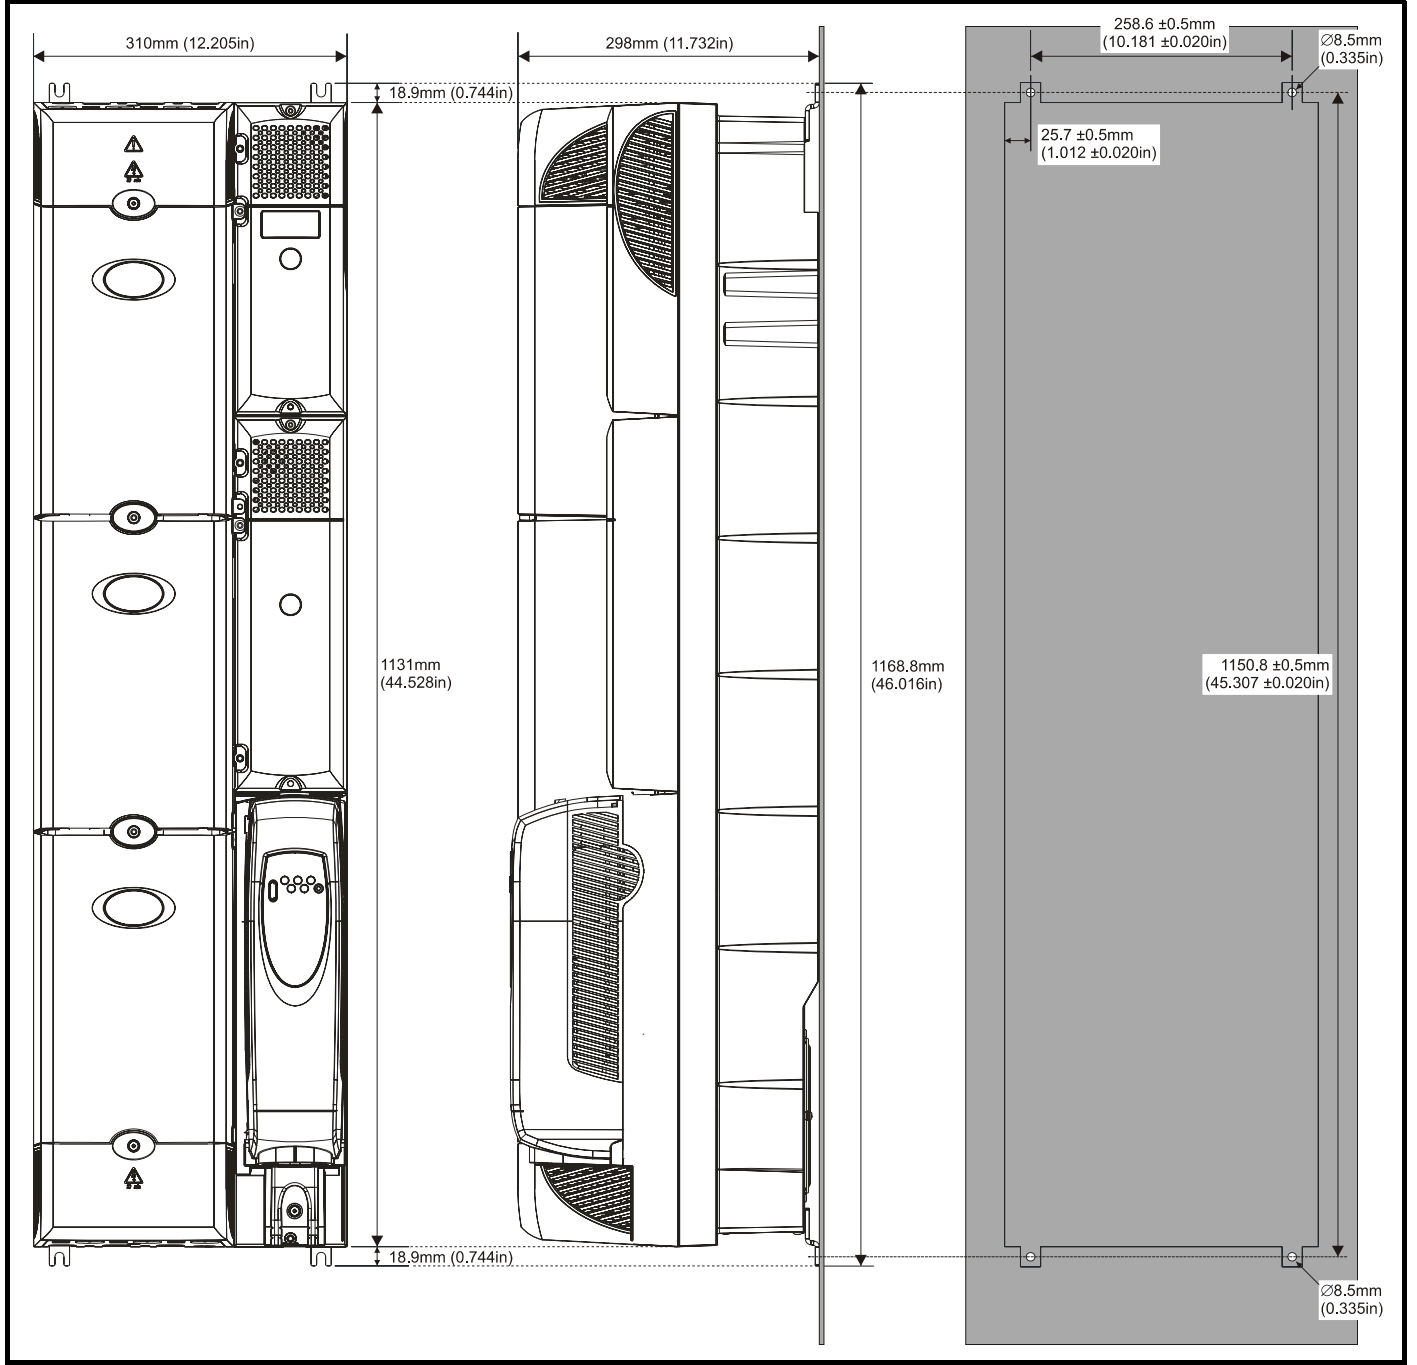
Boy 4 sürücülerin yüzey montajı
